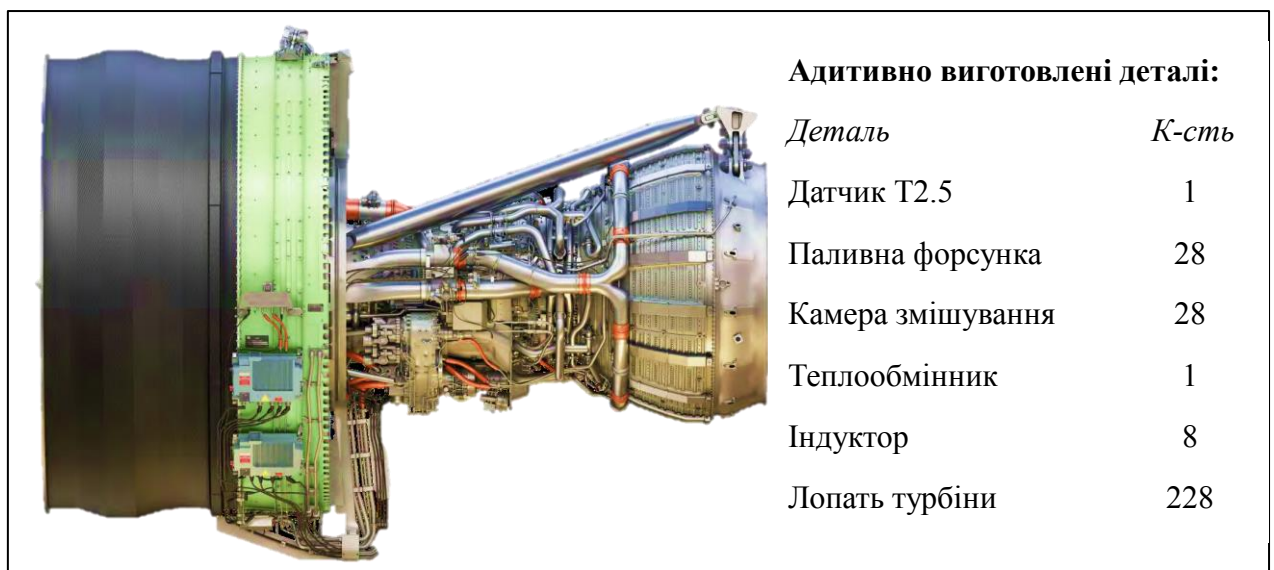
Адитивно виготовлені деталі в конструкції двигуна GE9X [4]
